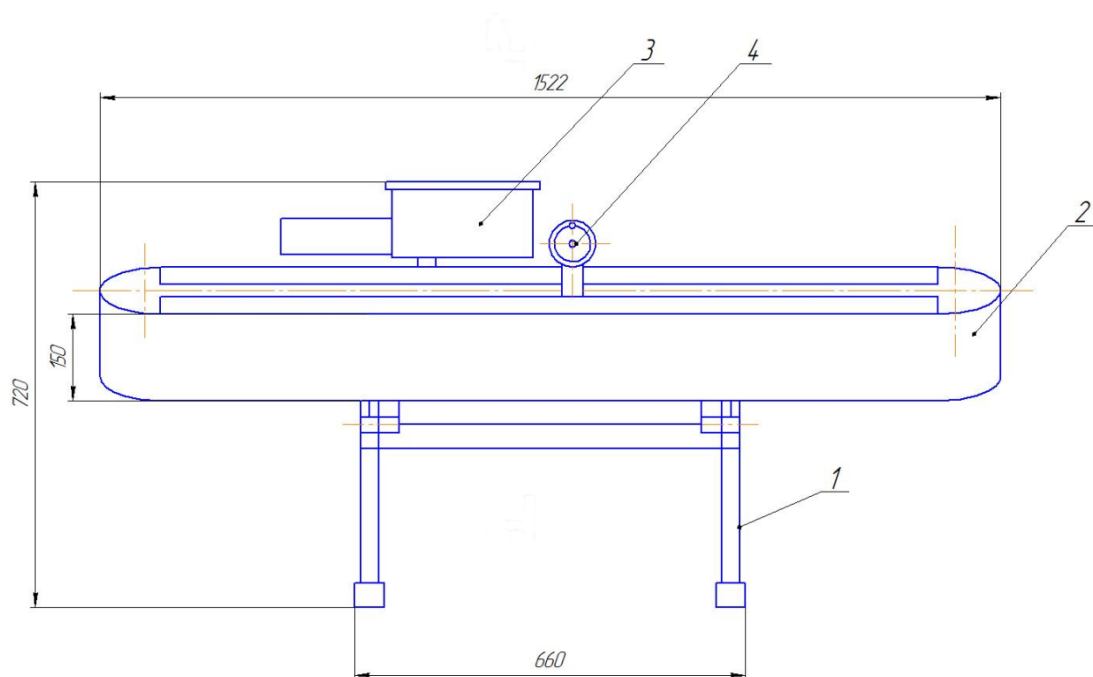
Общий вид ленточного округлителя ОЛ-2М: 1– станина; 2 – лента; 3 – мукопосыпатель; 4 – регулятор развала транспортеров; 5 – моторредуктор.
